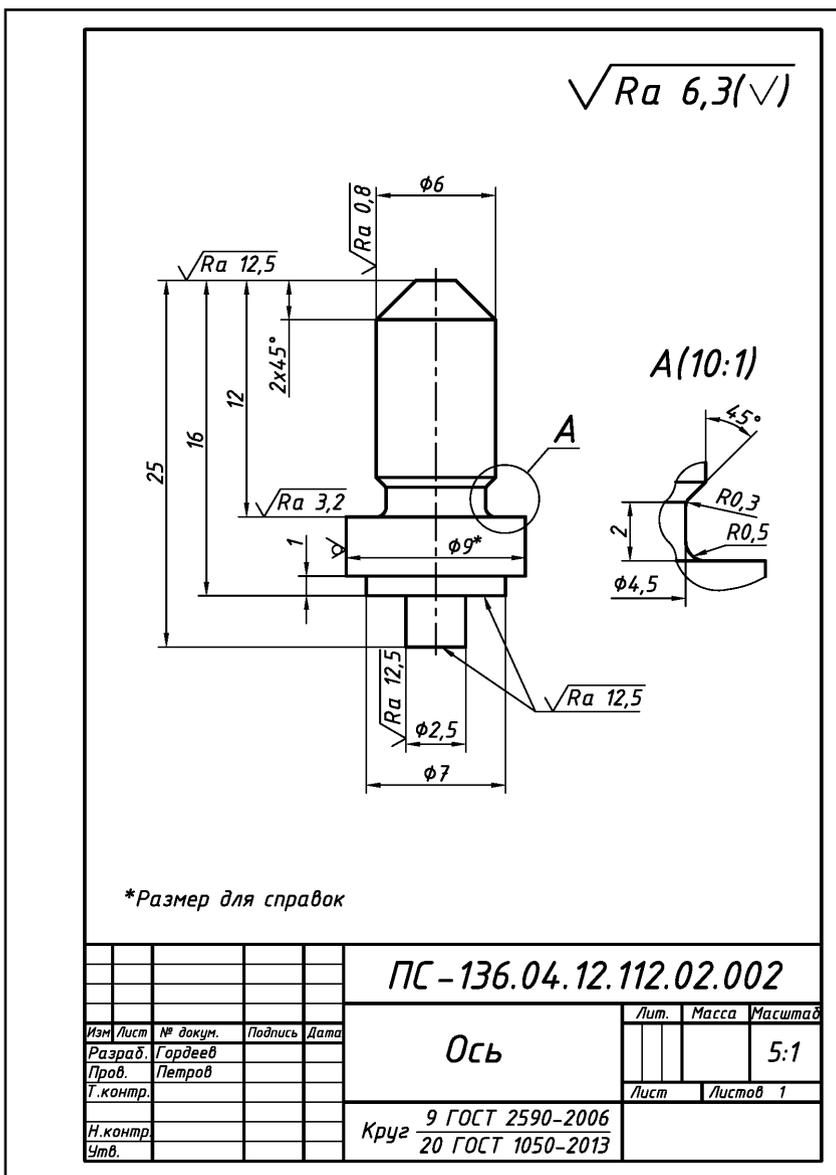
Оформление рабочего чертежа детали «Ось» сборочной единицы «Опора подшипника» (рис. 1.68)
